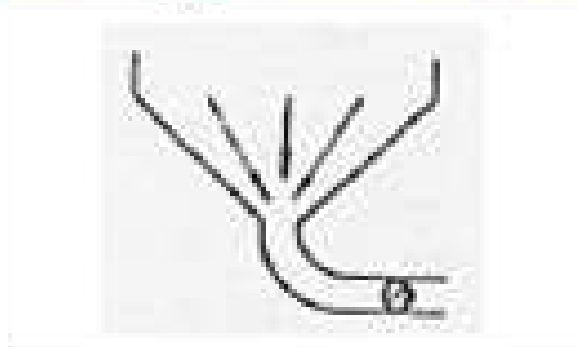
Captor para as máquinas: Serra de Fita ou (Serra de Corte) e Serra Circular.
